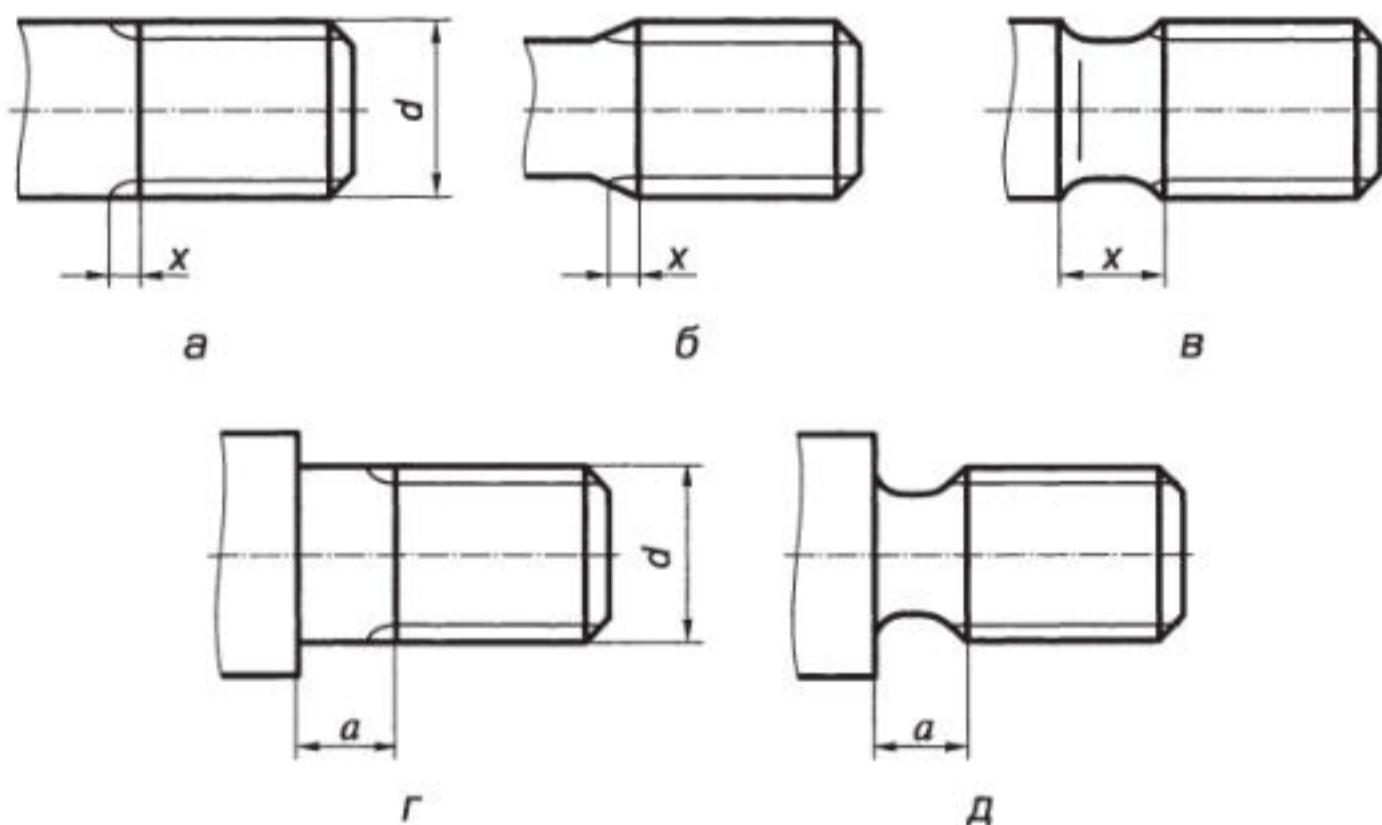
Сбеги и недорезы наружной метрической резьбы при изготовлении нарезанием [а, г] и накатыванием [б, в, д]
